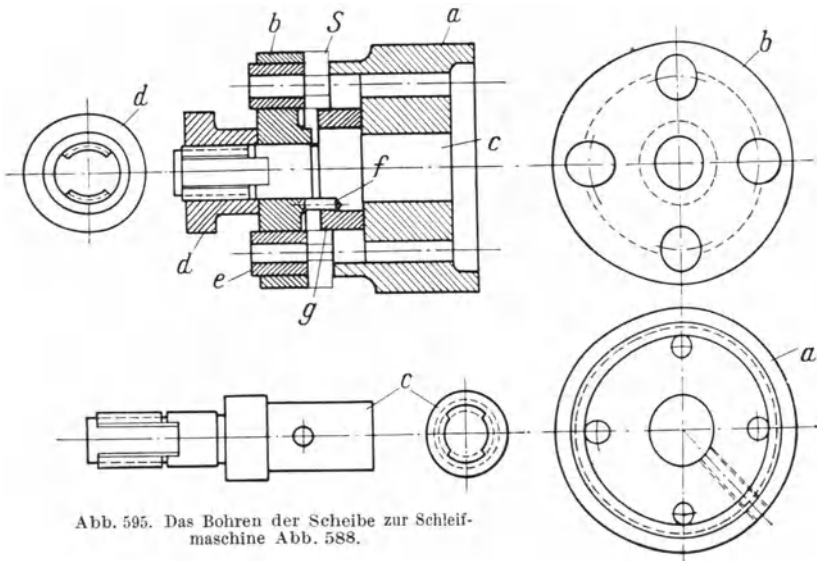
Das Bohren der Scheibe zur Schleifmaschine Abb. 588.
